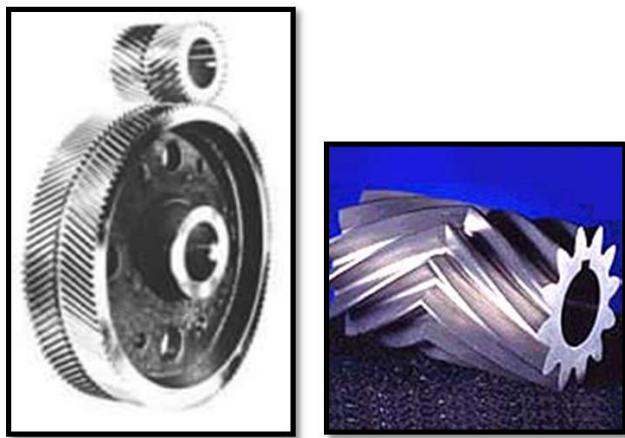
Engrane helicoidal doble (izquierda) y espiga (derecha)
